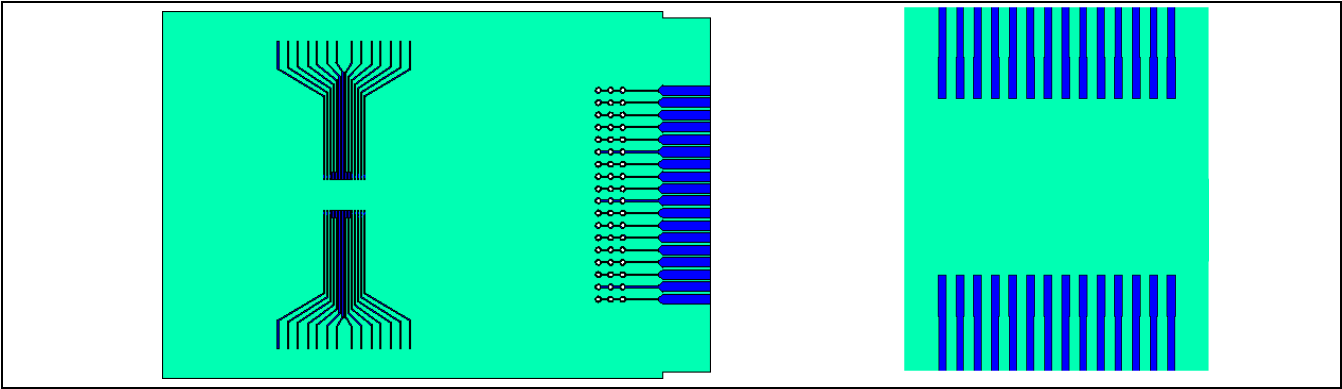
PCB 参考布局（根据 JEDEC 1s0P）
